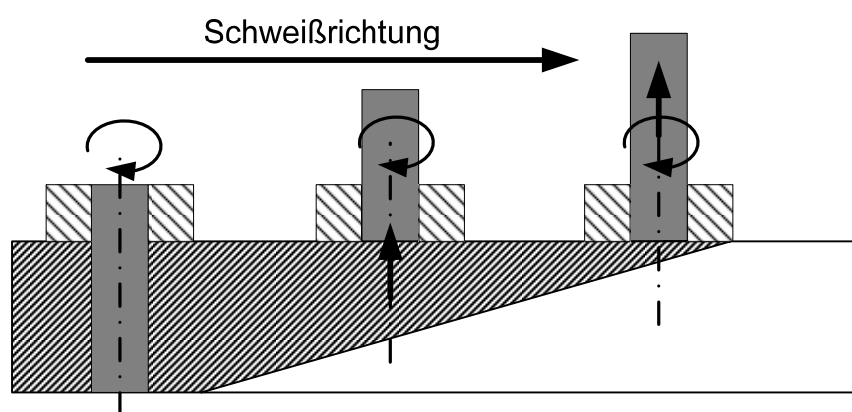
Retractable Pin Tool (Werkzeug bewegt sich in Vorschubrichtung)
